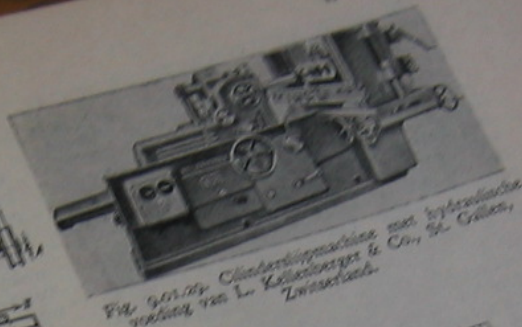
Cilinderslijpmachine met hydraulische voeding van L. Kellenschlager & Co., St. Gallen, Zwitserland.
